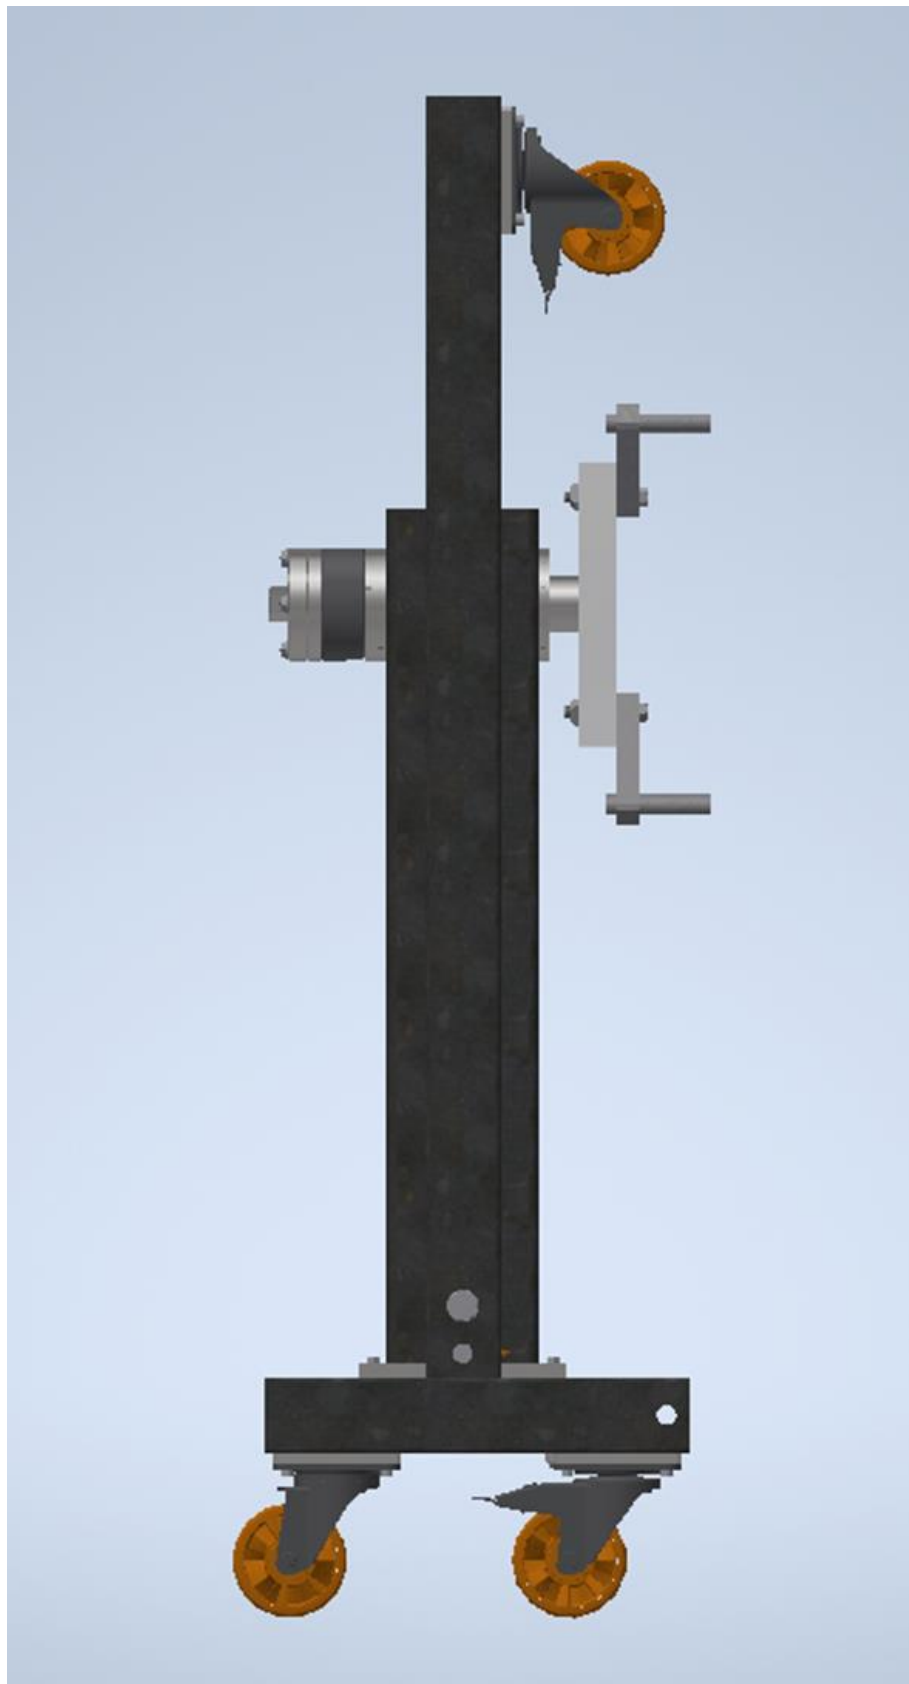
Motor-Montagevorrichtung Mobile Seitenansicht
